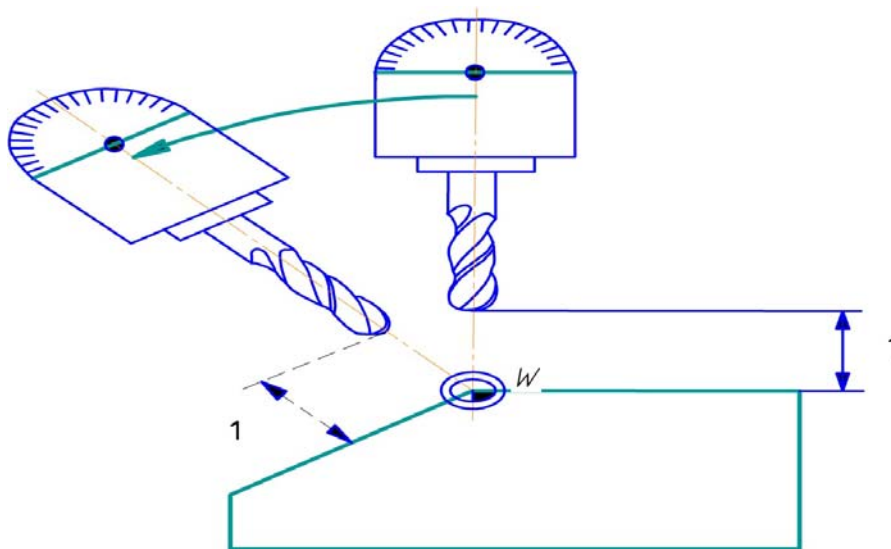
Поворот инструмента относительно центра, лежащего на плоскости заготовки
